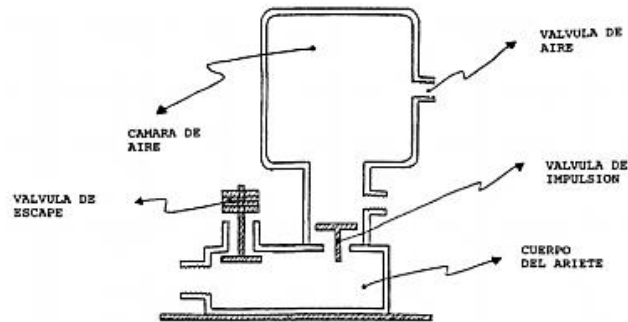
Cámara de aire y componentes de un ariete hidráulico.
